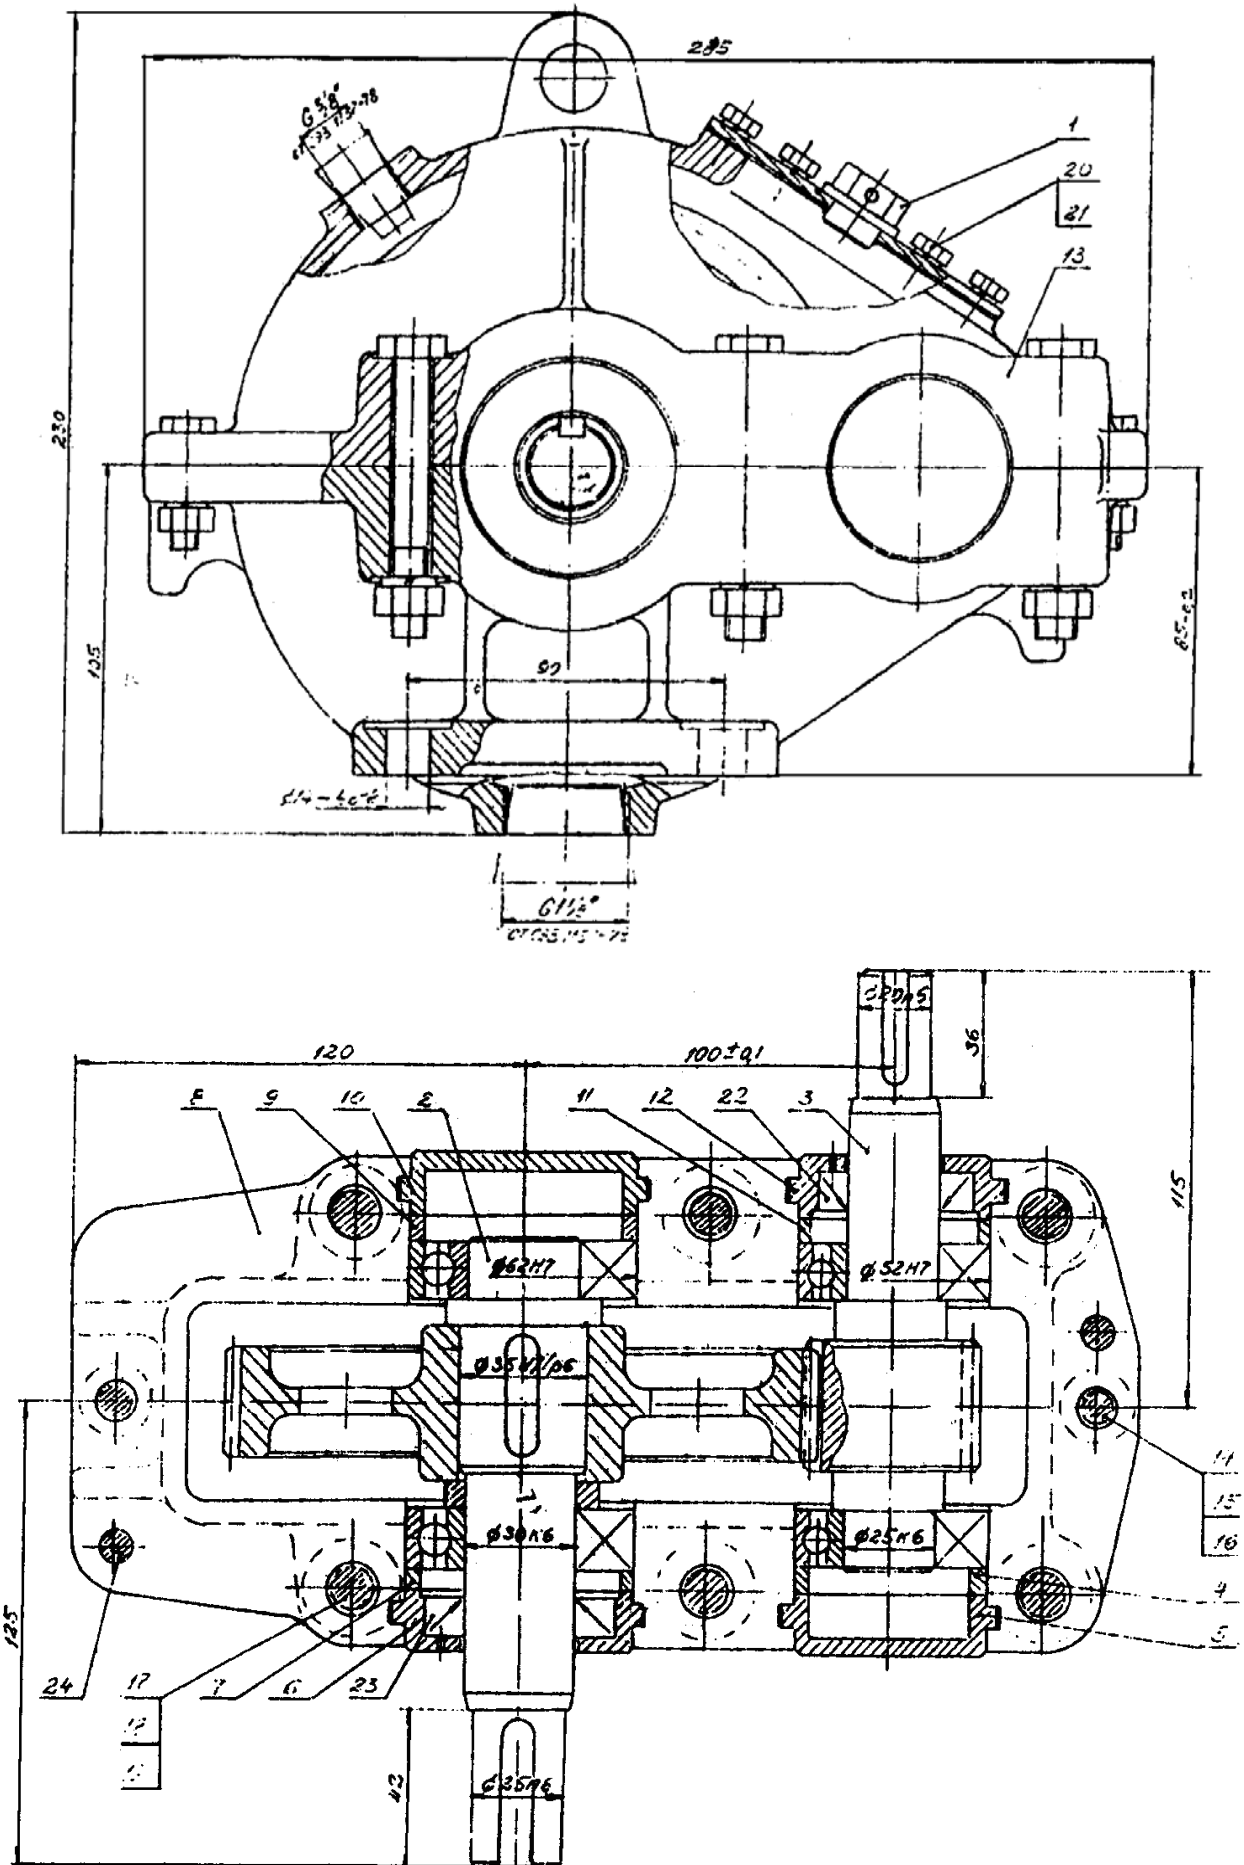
Редуктор циліндричний одноступінчастий прямозубий
